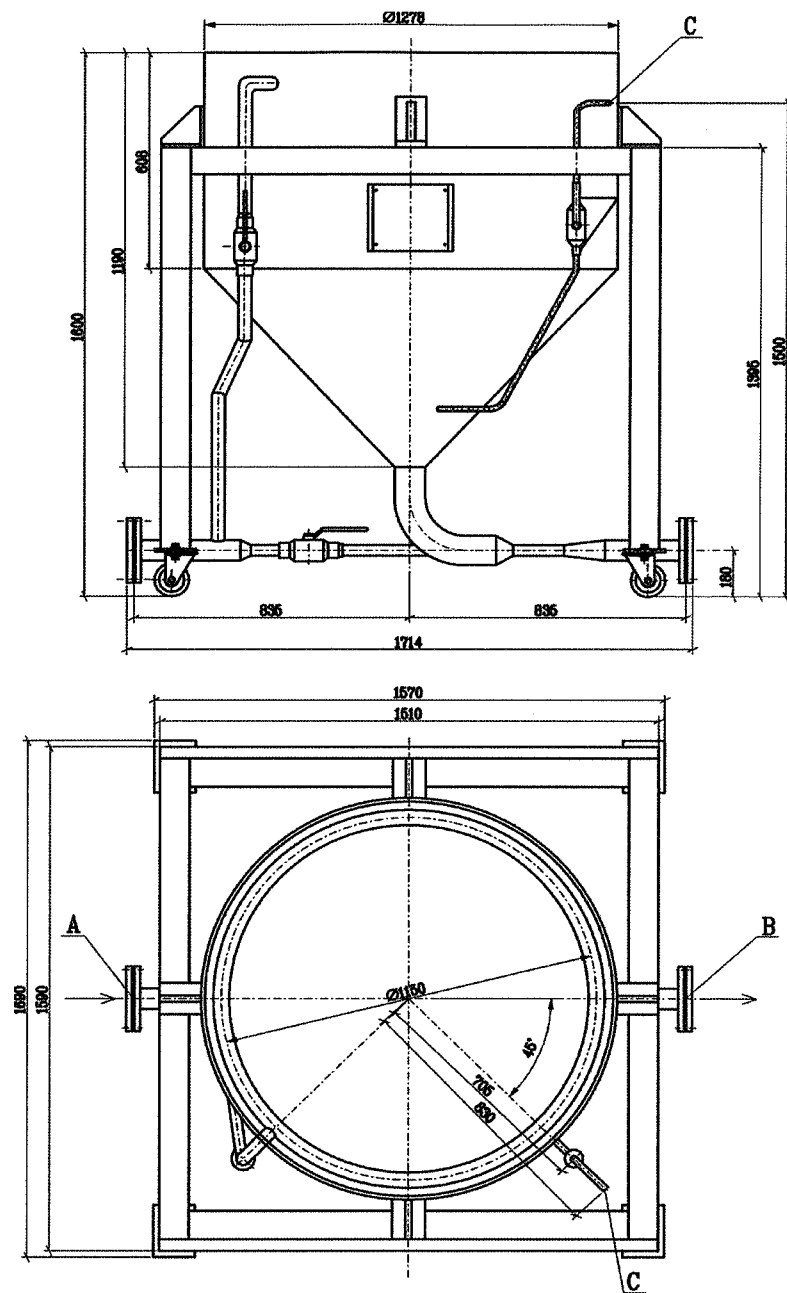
Габаритный чертеж гидротранспортера LDB01AF001
